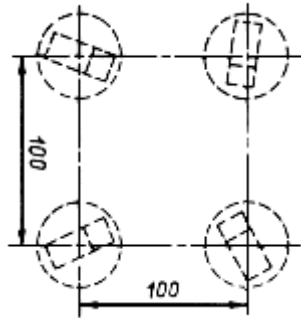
Схема контроля основного металла корпуса реактора (в каждой точке искатель поворачивают на 360°)
